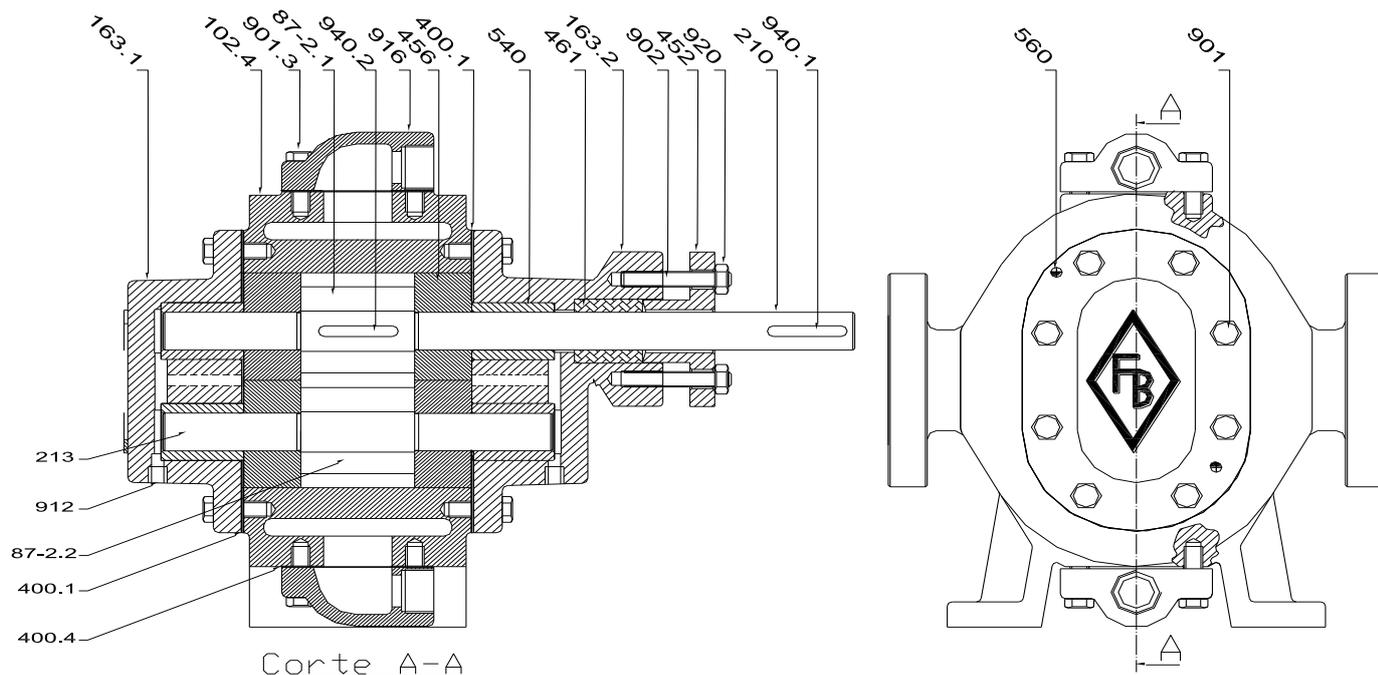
Desenho em Corte bomba FBE c/ Câmara
